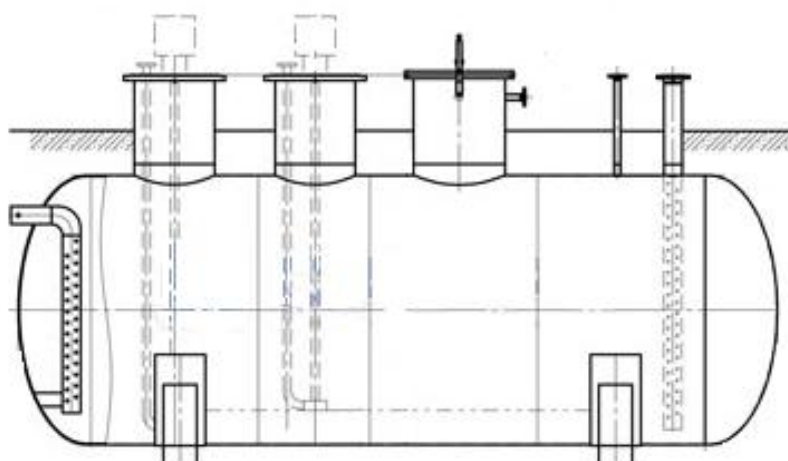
Эскиз конструкции резервуаров ЕП – 25 №№ 26, 27, 39, 40
